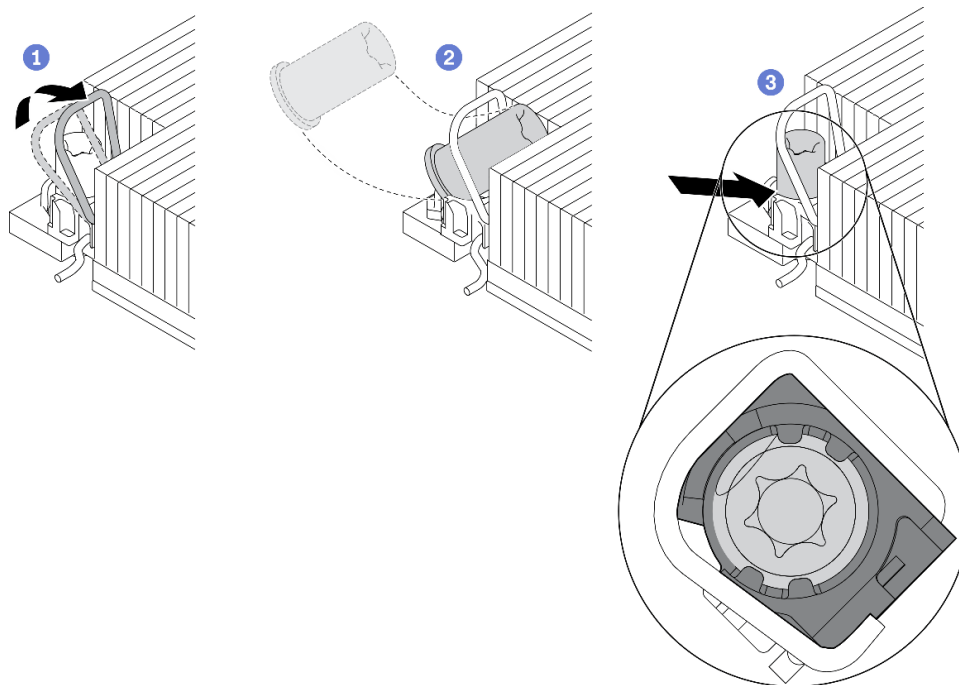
Installation d'une douille Torx T30 dans le dissipateur thermique
